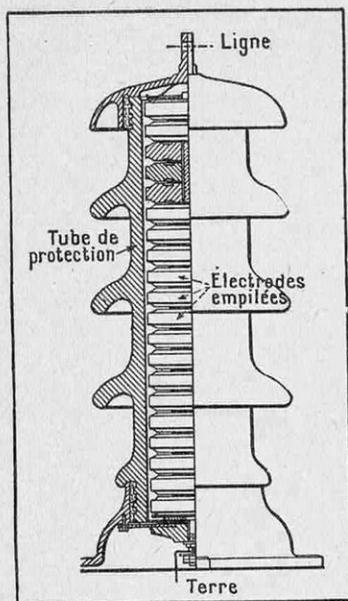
COUPE D'UN PARAFONDRE LS A HAUTE TENSION
